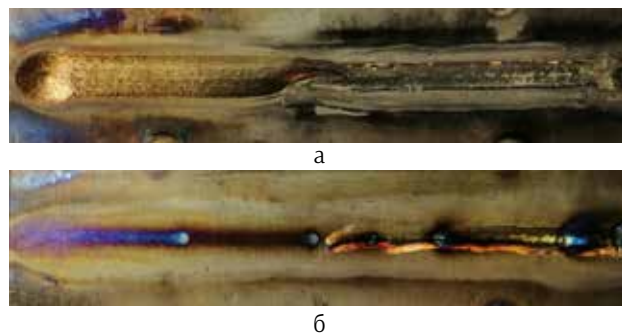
Фото лицевой и корневой стороны шва после сварки по слою флюса вольфрамовым электродом, справа – участок, предварительно покрытый флюсом, слева – участок чистого титана: а – лицевая сторона; б – корневая сторона
